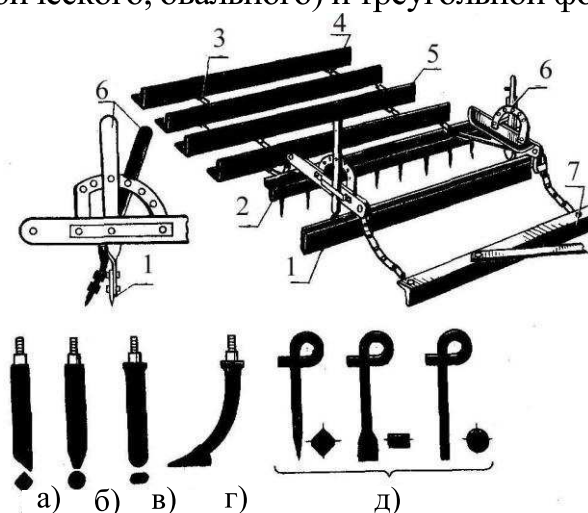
Общий вид шлейф-бороны ШБ-2,5: 1 – нож; 2 – грабли; 3 – шлейф; 4 – цепочка; 5 – стальной уголок; 6 – рычаг; 7 – брус; а – зуб квадратного сечения; б – зуб круглого сечения; в – зуб овального сечения; г – лапчатый зуб; д – зубья сетчатой бороны
